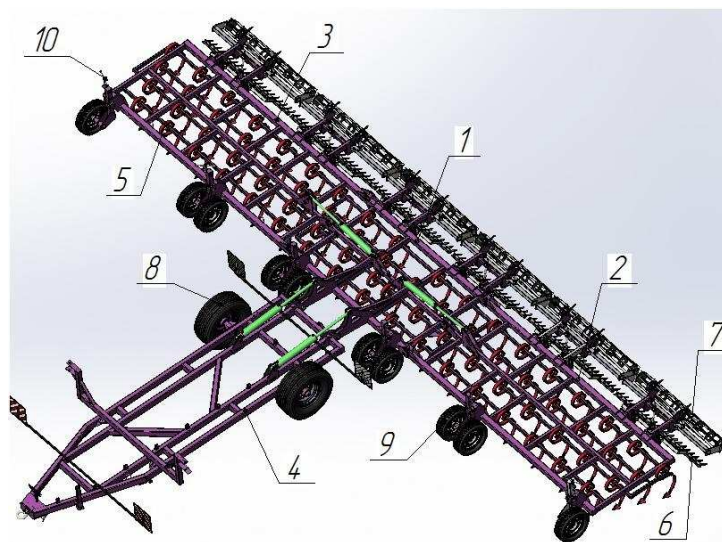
Общий вид культиватора Кусто-12М. 1- основная рама; 2-левое крыло; 3-правое крыло; 4- дышло; 5-инструментальная рама; 6 -разрыхлитель; 7 -каток прикатывающий; 8 -транспортное колесо; 9 - технологические колеса; 10 -регулировочный винт
